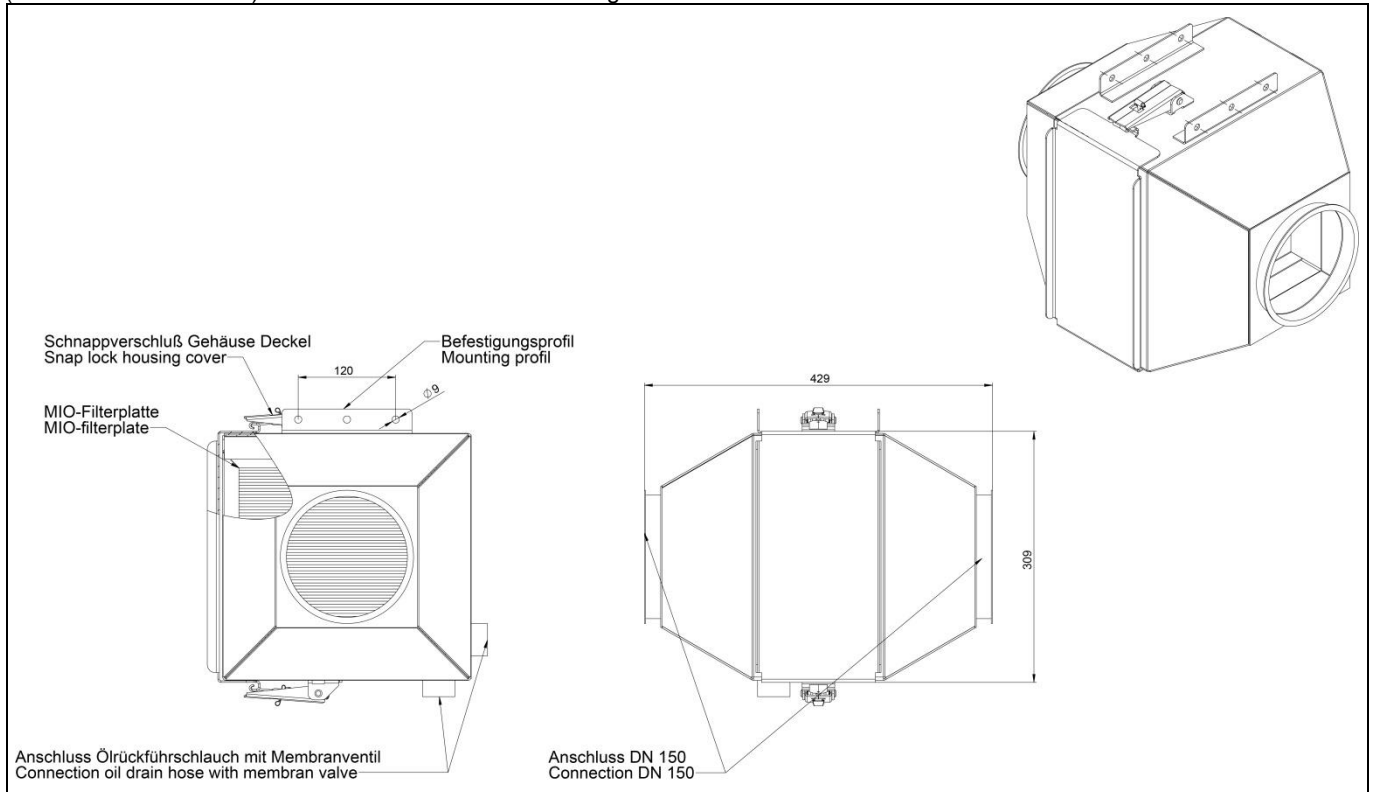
Montage einer Filterplatte außerhalb einer Bearbeitungsmaschine
